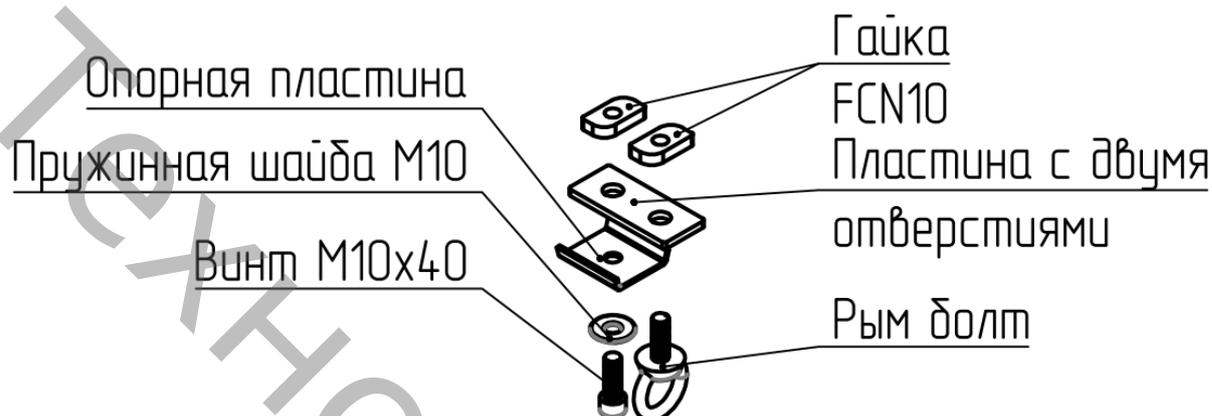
Сборка крепления рым-болта. СПМ, исполнение 1 и 2.
